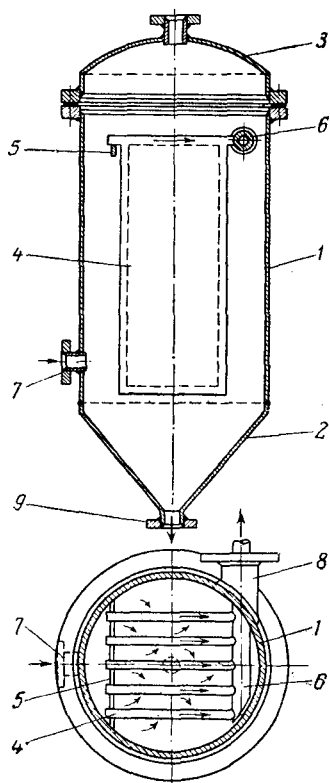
Листовой фильтр с вертикальным цилиндрическим резервуаром:
